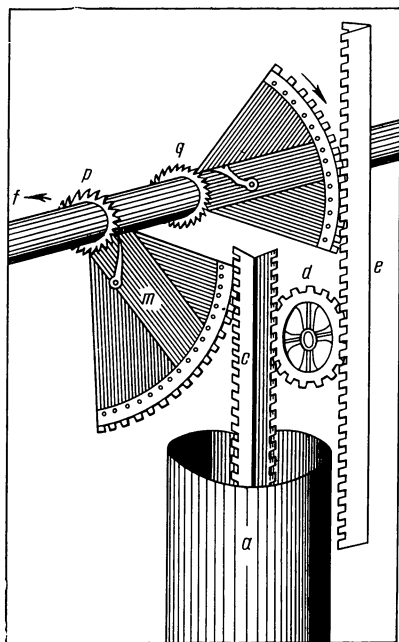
Старинный чертеж механизма получения непрерывного однонаправленного вращения вала от периодически действующего цилиндра пароатмосферного двигателя, предложенный Фицджеральдом в 1759 г.
